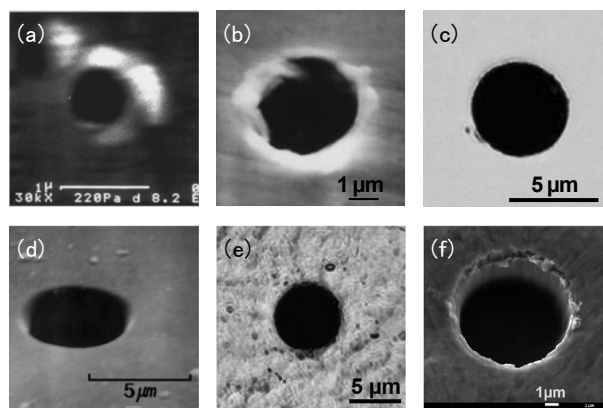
各種材料加工法による極小穴あけ加工例((a)放電加工 (b)切削 (c)研削 (d)超音波加工 (e)電解加工 (f)打抜き)
